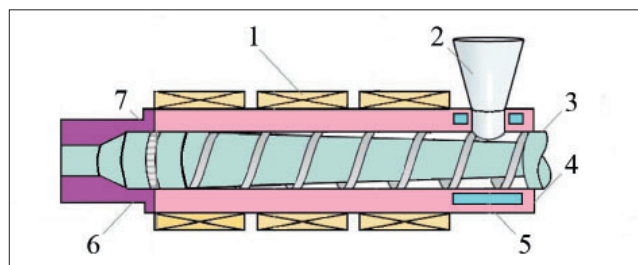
Зерновой пресс-экструдер (общий вид): 1 – нагреватель; 2 – бункер; 3 – шнек; 4 – цилиндр; 5 – полость для циркуляции воды; 6 – формирующая головка; 7 – решетка с сетками
